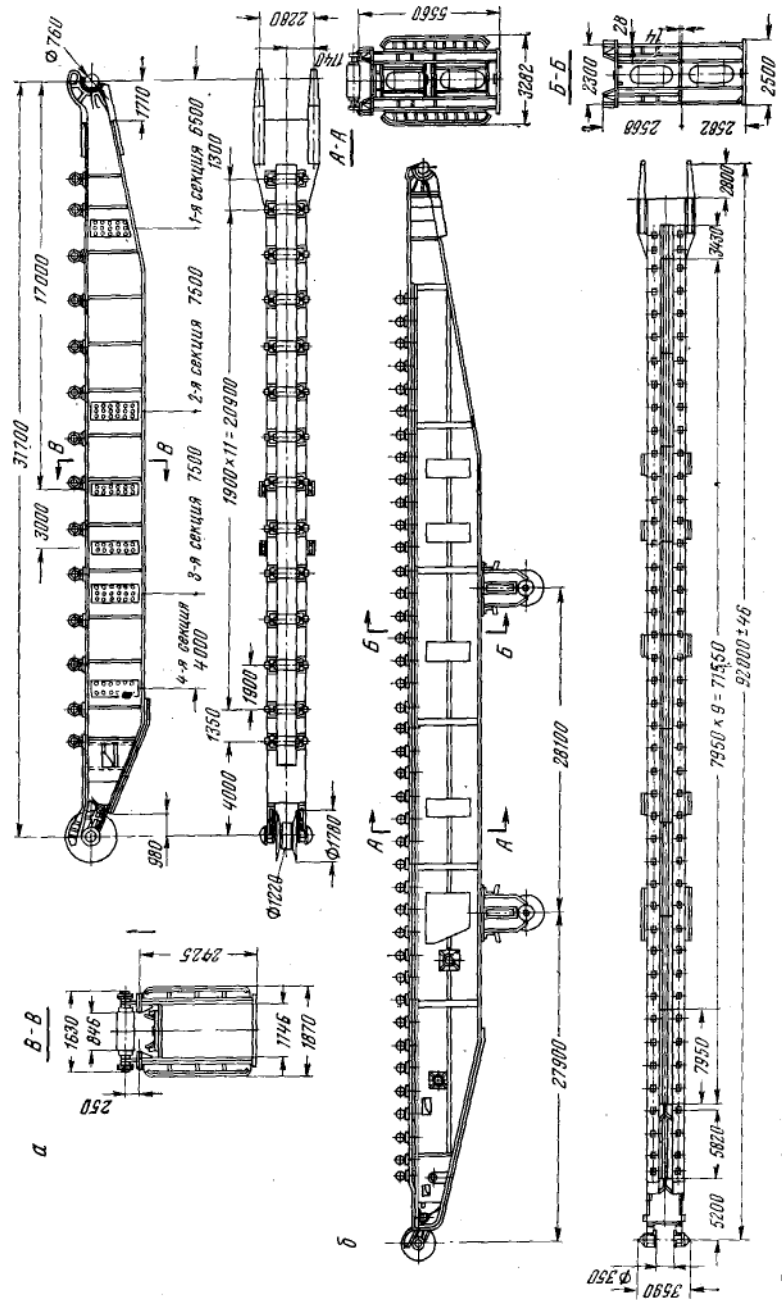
Общий вид конструкции черпаковой рамы драг 250Д (а) и 600Д (б) с двумя поддерживающими ба-
